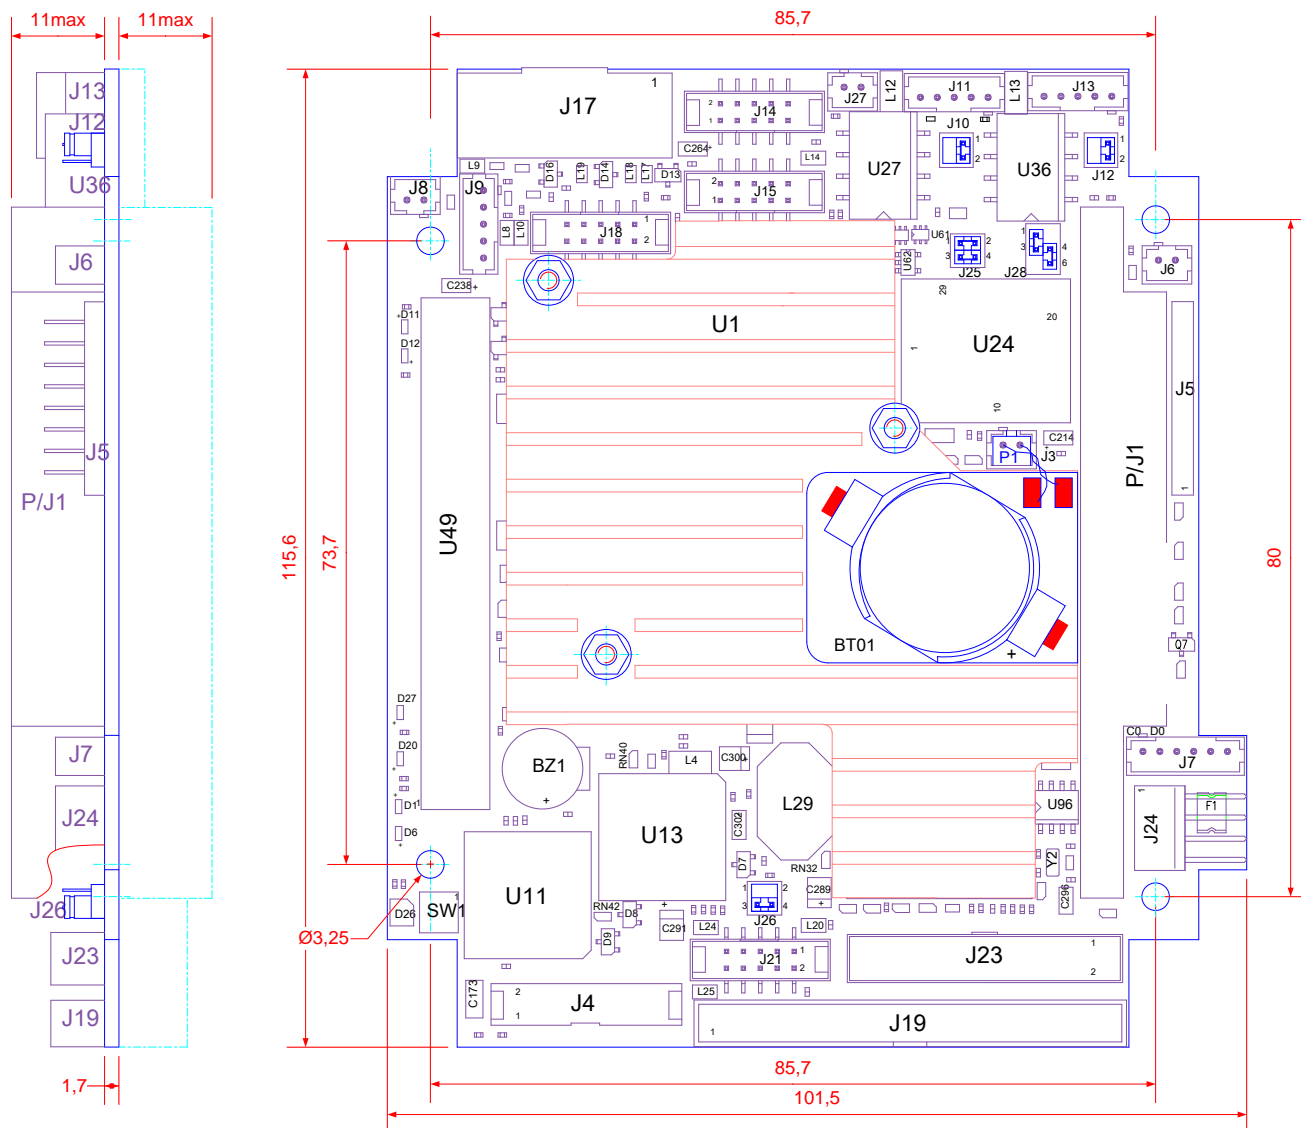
Габаритные и присоединительные размеры модуля
